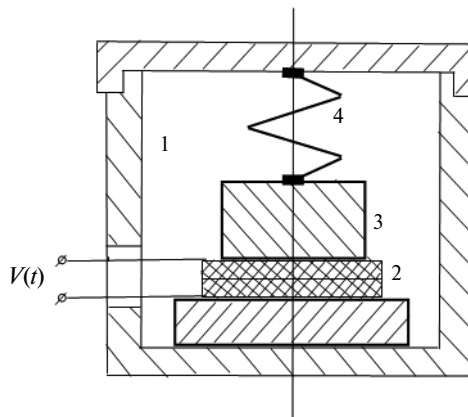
Схематический чертёж конструкции пьезоакселерометрического датчика виброускорений
